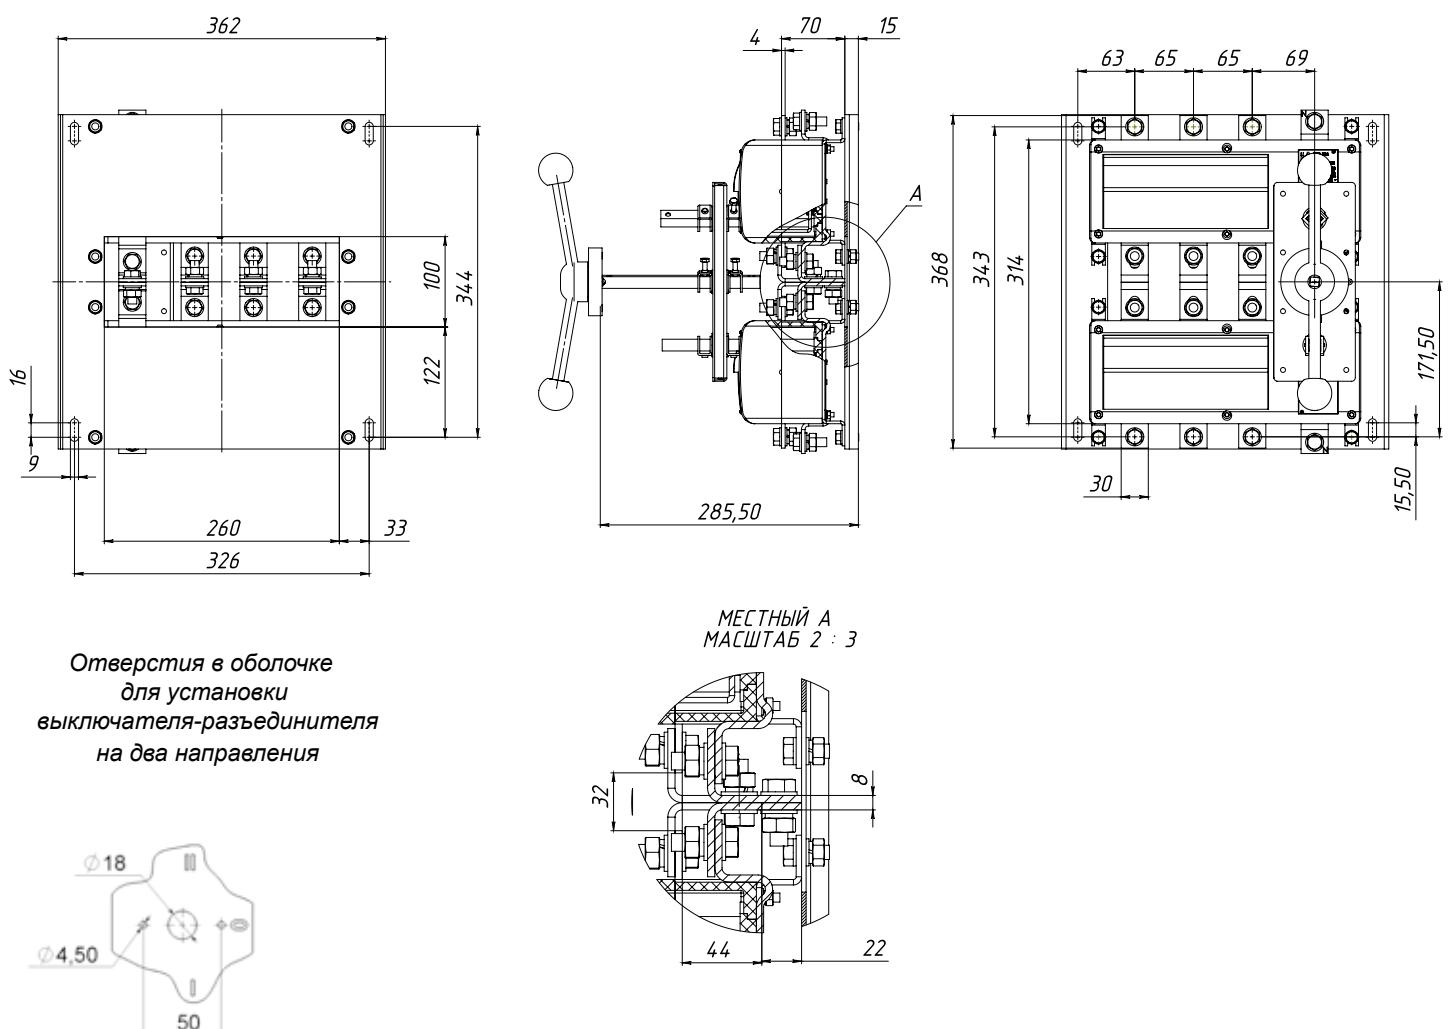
Выключатель-разъединитель ВНК-35-71130-32 УХЛЗ
